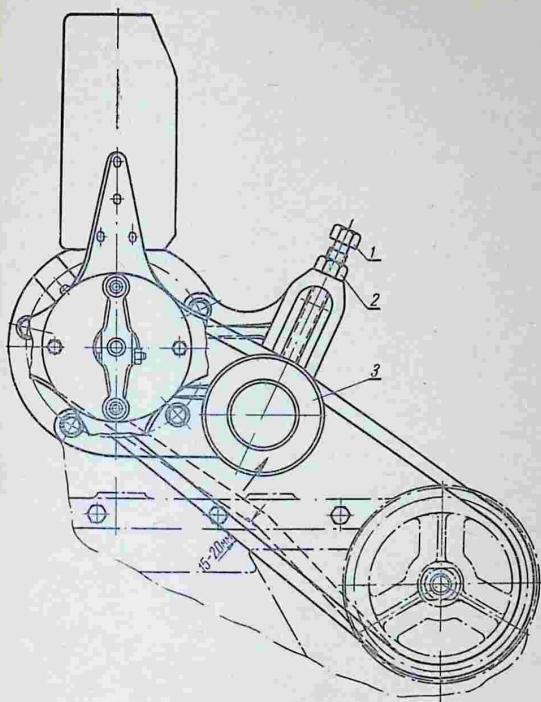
Проверка натяжения ремня вентилятора двигателя Д-54А:
